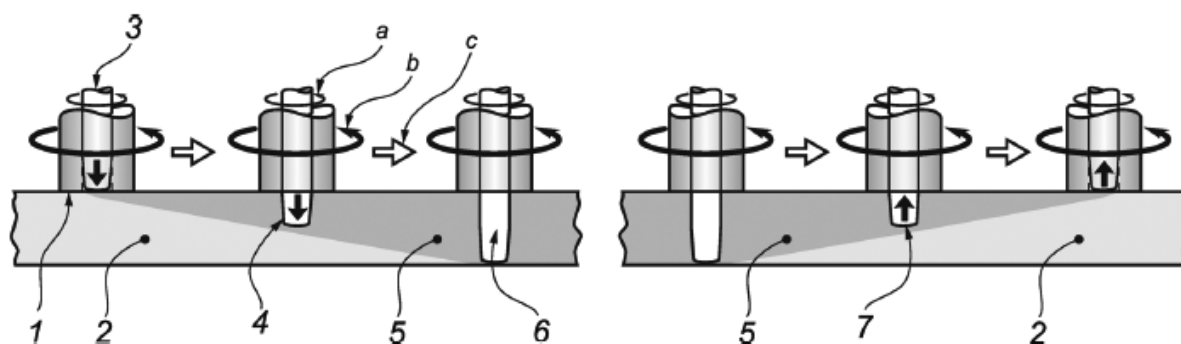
Схема начала и завершения сварки кольцевого шва с образованием выходного отверстия над линией стыка в основном металле [7]
